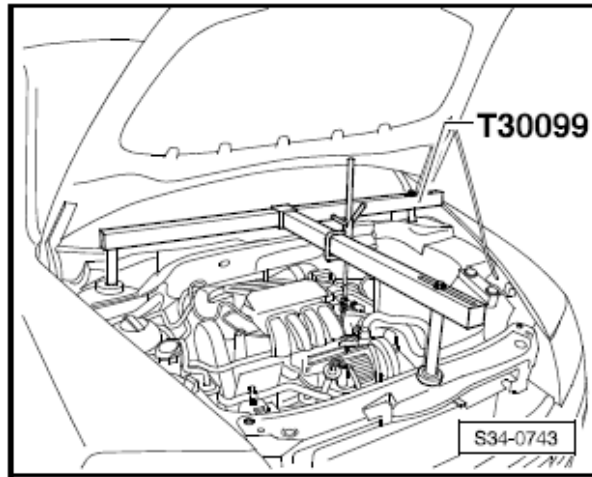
Схема встановлення підвісного закріплювального пристрою T30099
